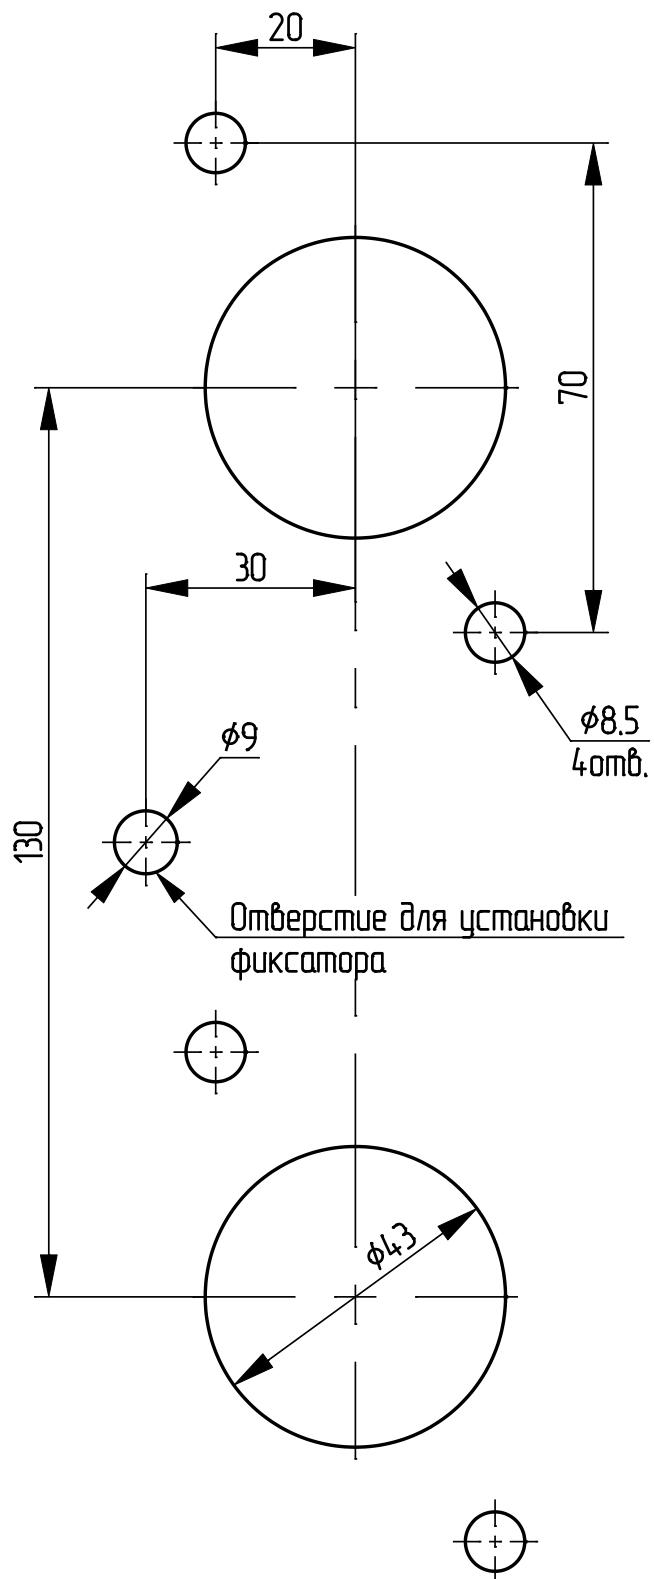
Разметка отверстий для установки приводов ПРК-10Б с фиксатором (вид спереди)
